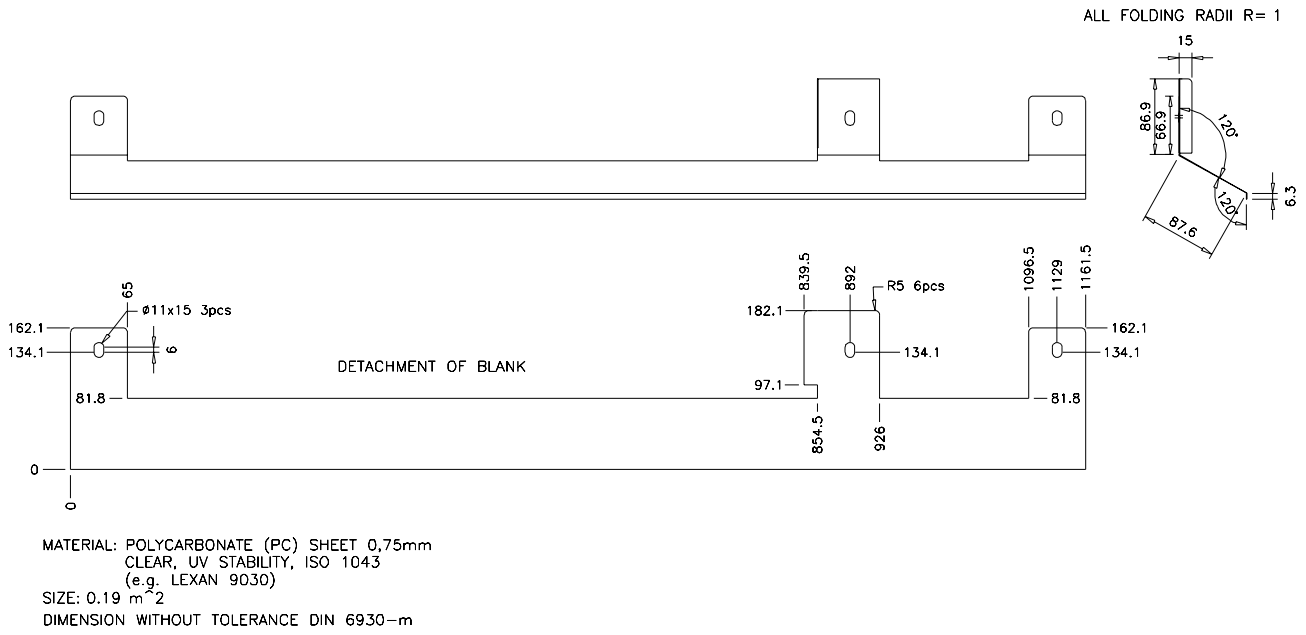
在外形尺寸 R12i 直流母排之间的绝缘体的尺寸
